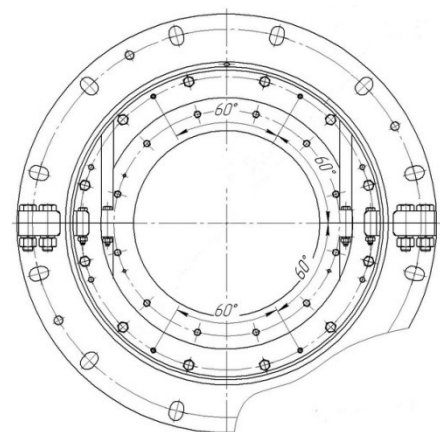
МРГК підшипникового вузла. Вид спереду.
